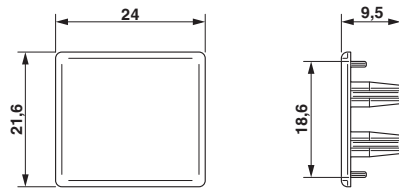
Dimensions de TMC 8 B2/3 END CAP
